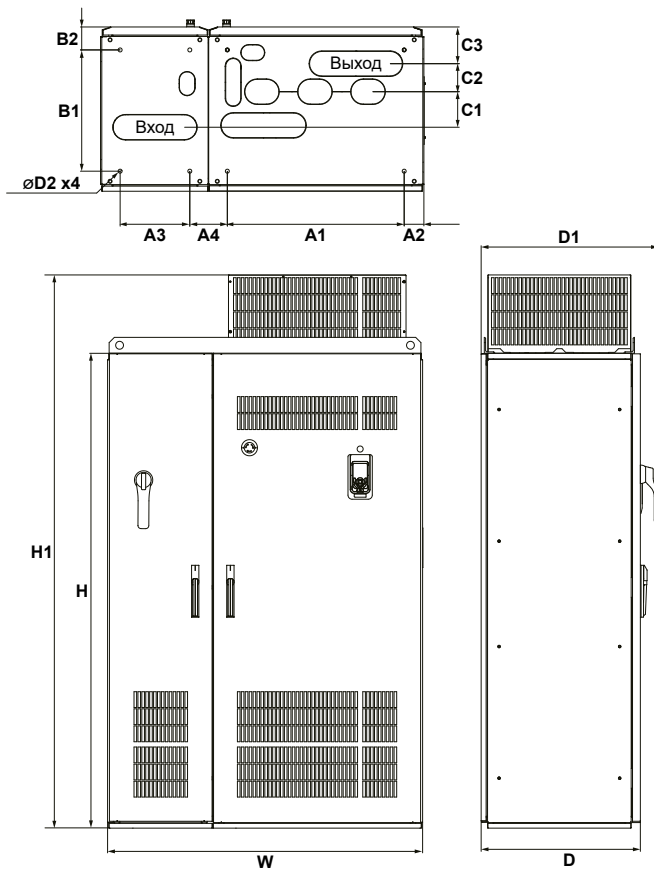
Внешний вид типоразмера Т13 (с распределительным щитом)
